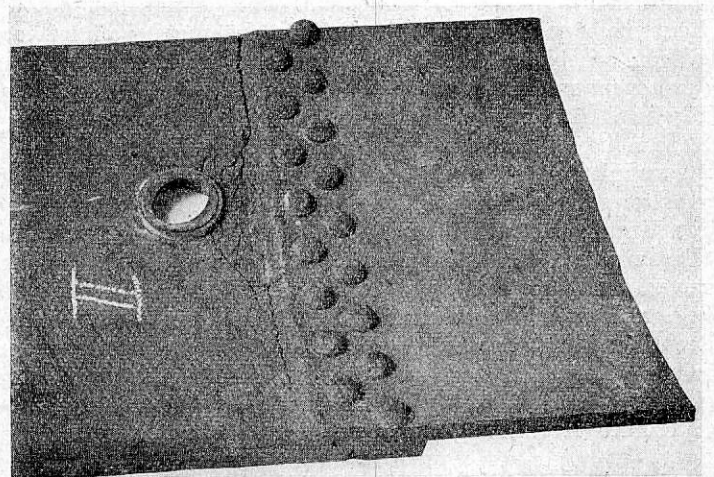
Erneut einsetzendes Kraftlinienrost an einer Stammkantenschweißung.
